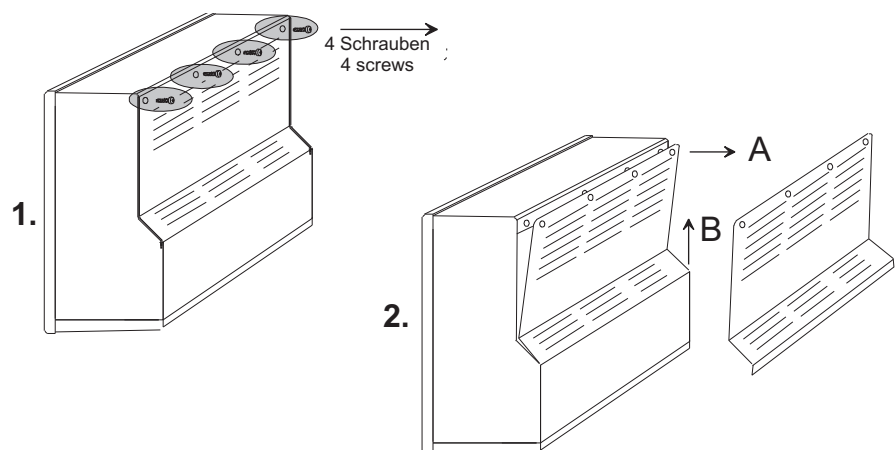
Entfernen des rückseitigen Abdeckblechs
